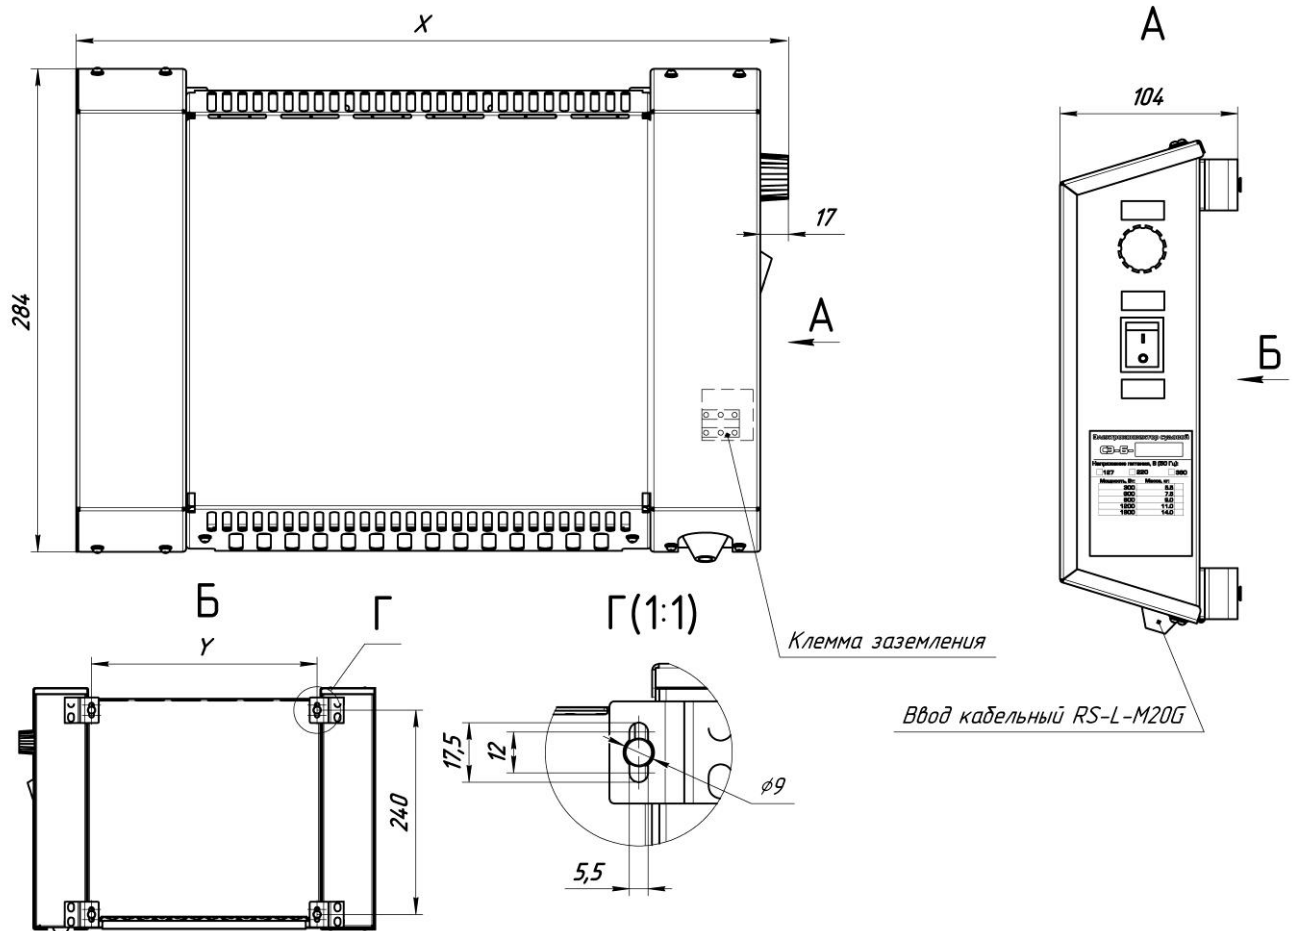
Габаритные и установочные размеры изделий типа СЭ-Б
